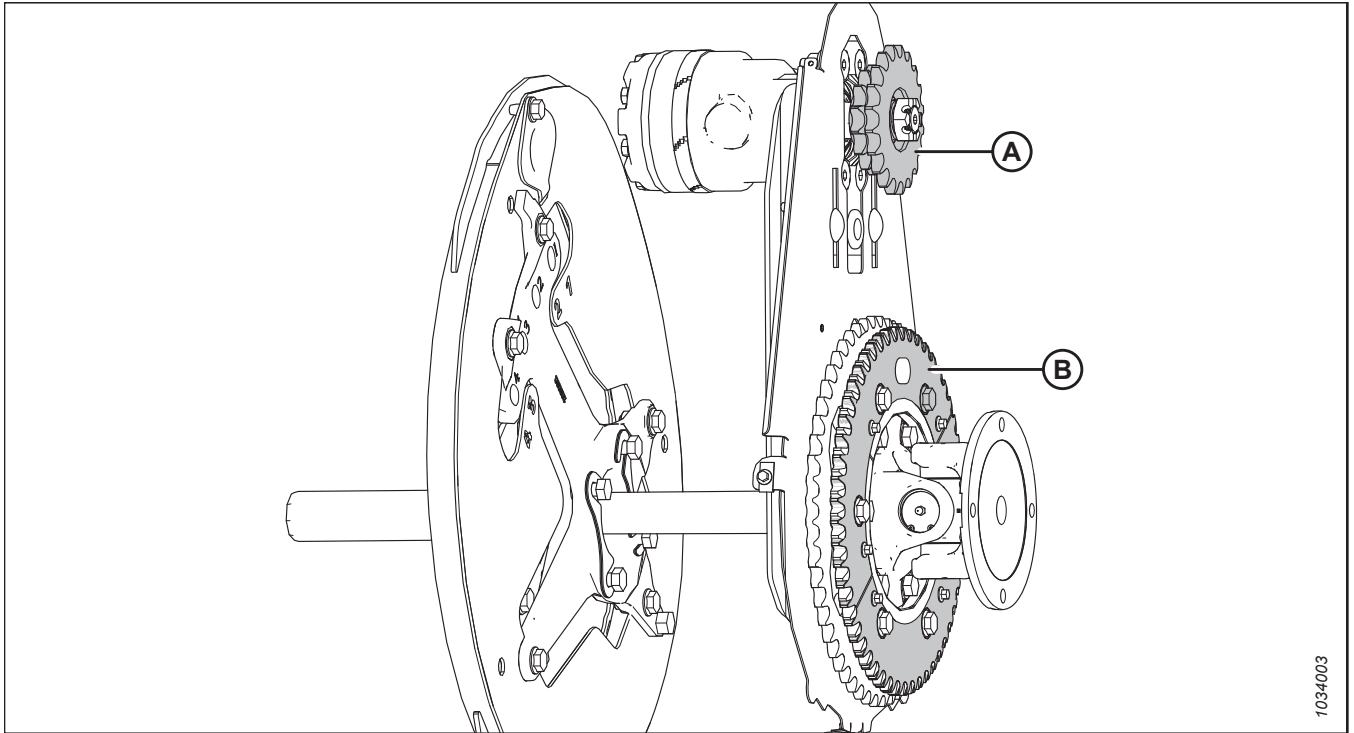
Привод мотвила с дополнительными звездочками
